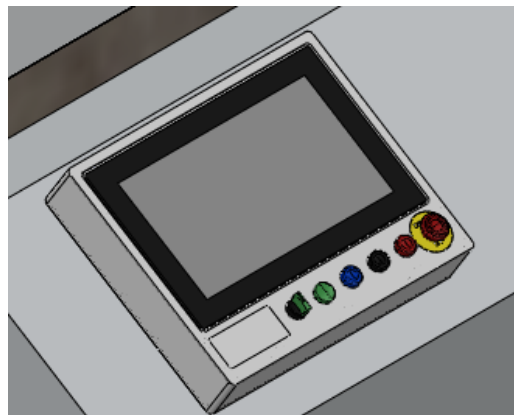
Control remoto con pantalla táctil de mesa posicionadora
